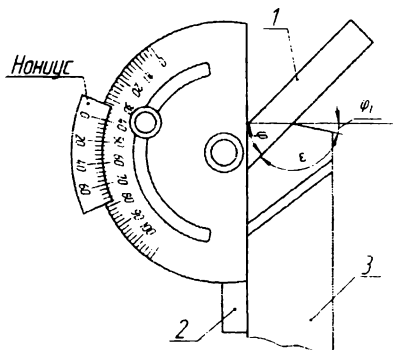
Схема измерения угла φ токарного проходного резца
